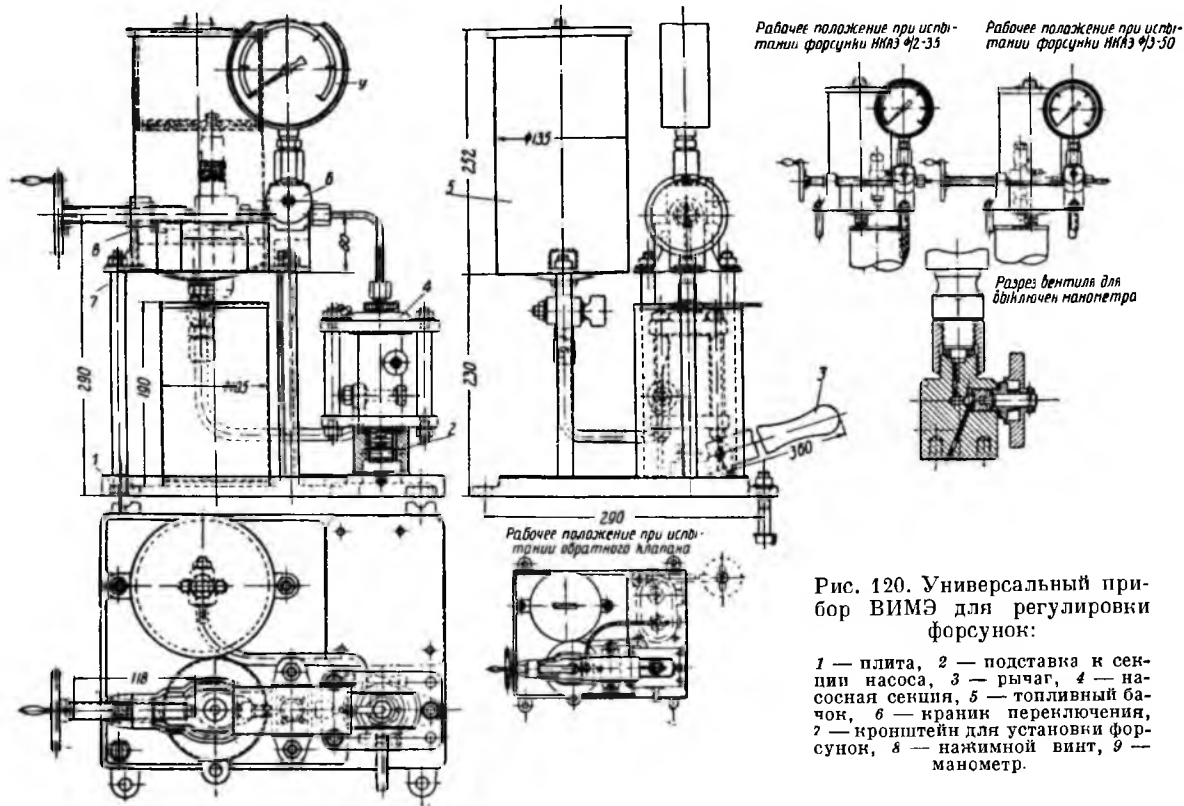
Универсальный прибор ВИМЭ для регулировки форсунок:
